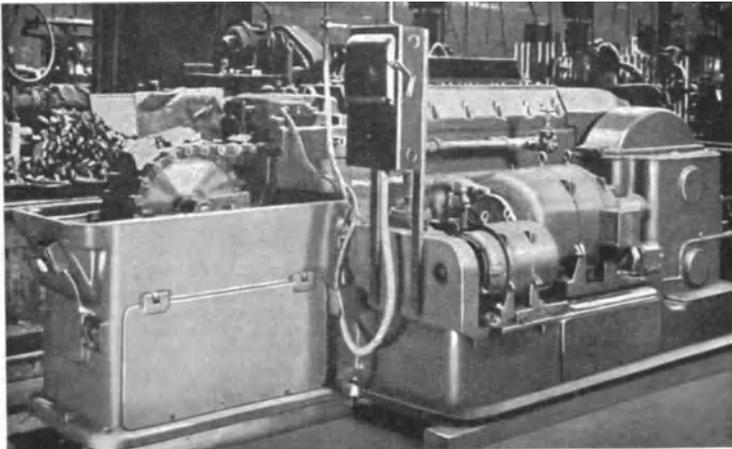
Außenräummaschine mit Kettenvorschub des Werkstücks.
